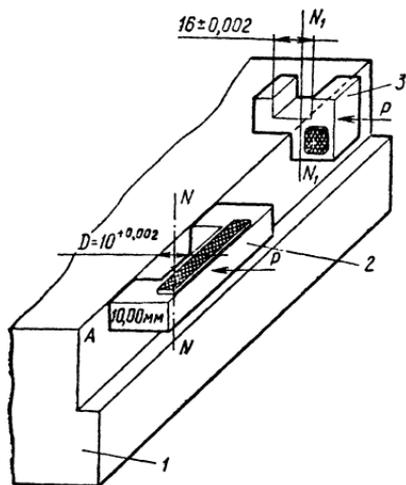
Приспособления для ориентации обрабатываемой заготовки посредством центроискателя на координатно-расточном станке:
